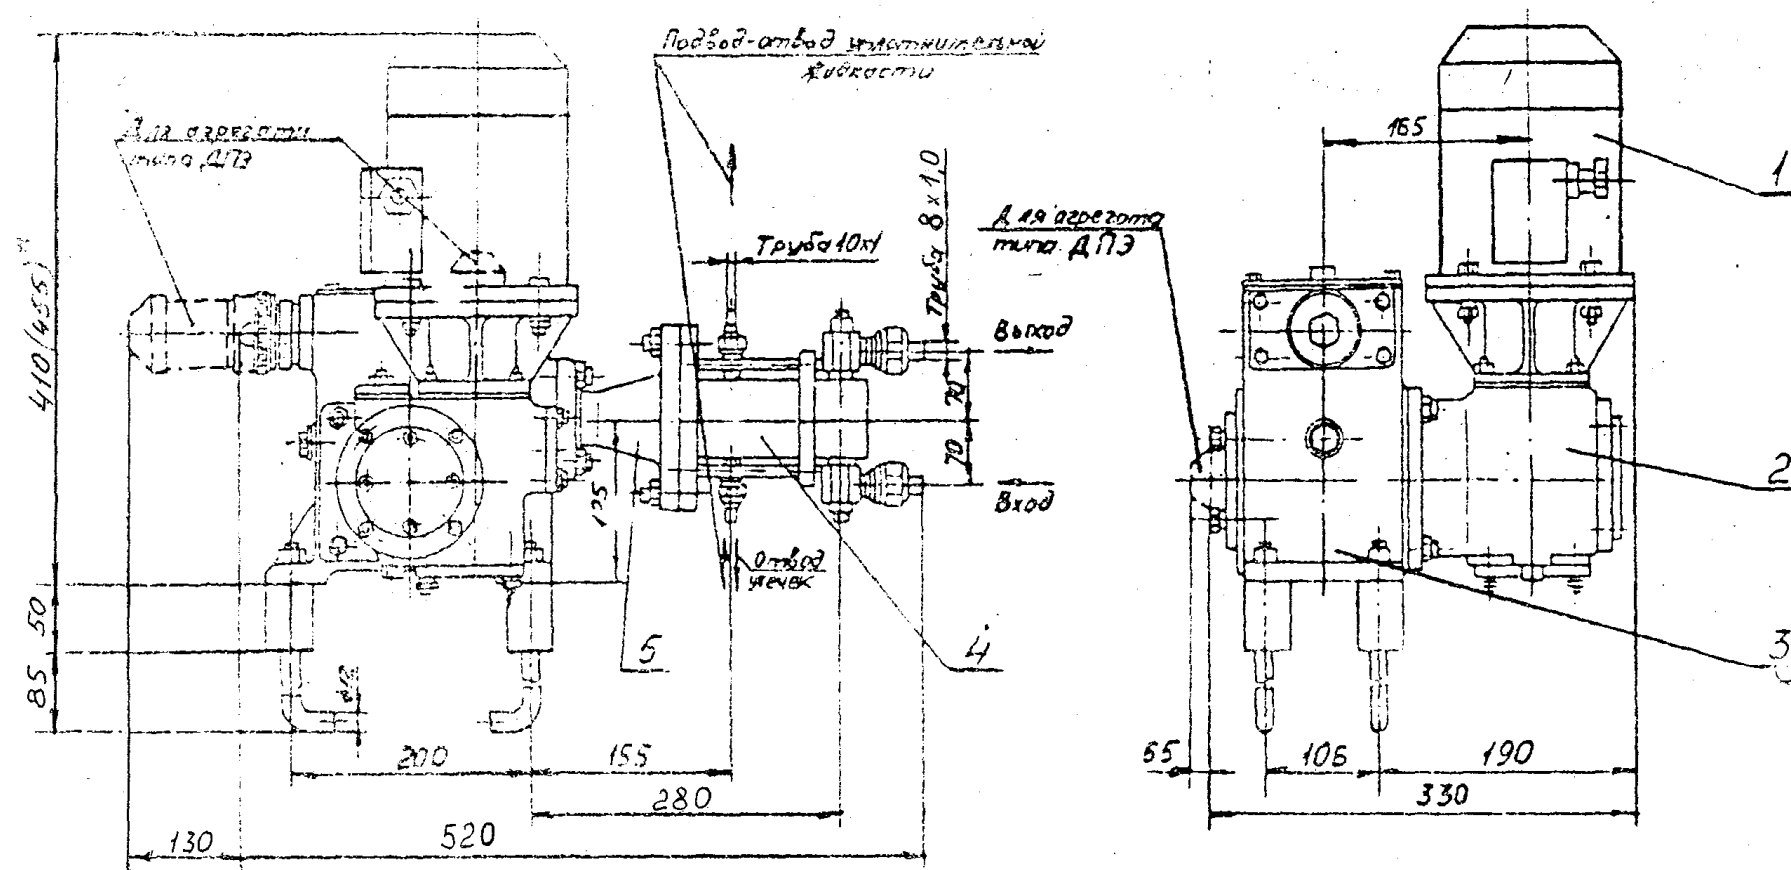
Габаритный чертеж насоса-дозатора гидразина LDN11AP001, LDN12AP001
